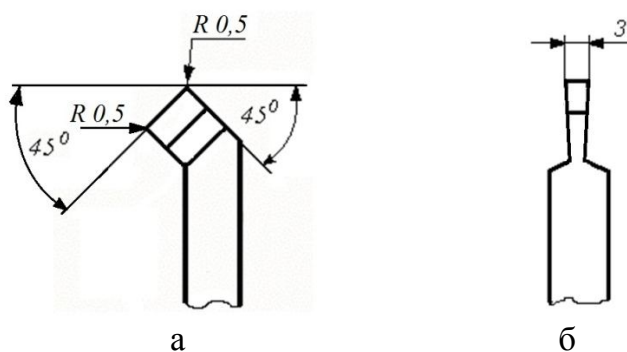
Схемы резцов: а – резец токарный проходной с отогнутой головкой; б – резец токарный отрезной
